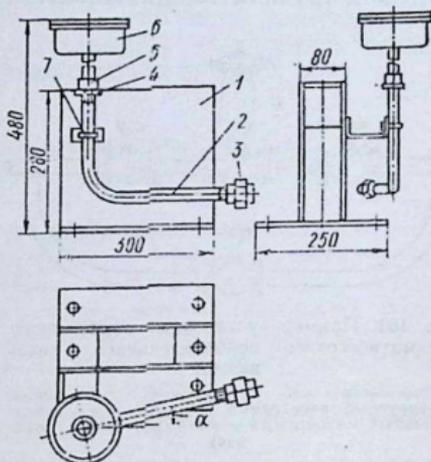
Конструкция для установки гидравлического исполнительного механизма:
